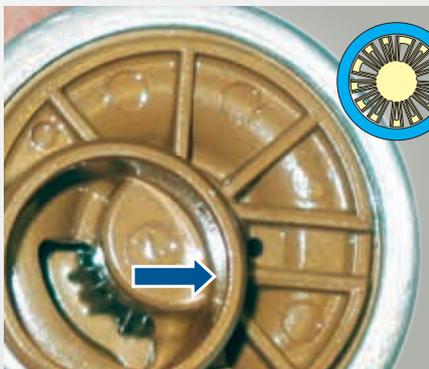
Les dents de la roue d'engrenage d'une pompe à canal latéral de type E1S ont été détruites par un corps étranger (ci-dessous).
